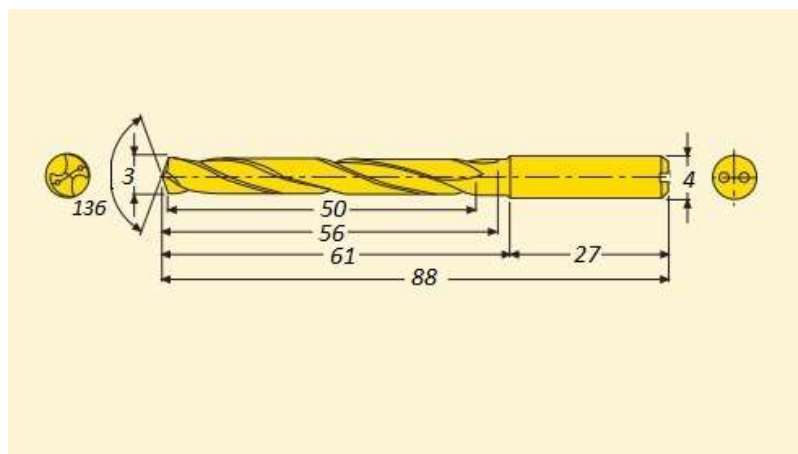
Сверло SecoFeedmax™ – SD216A-3.0-50-4R1
